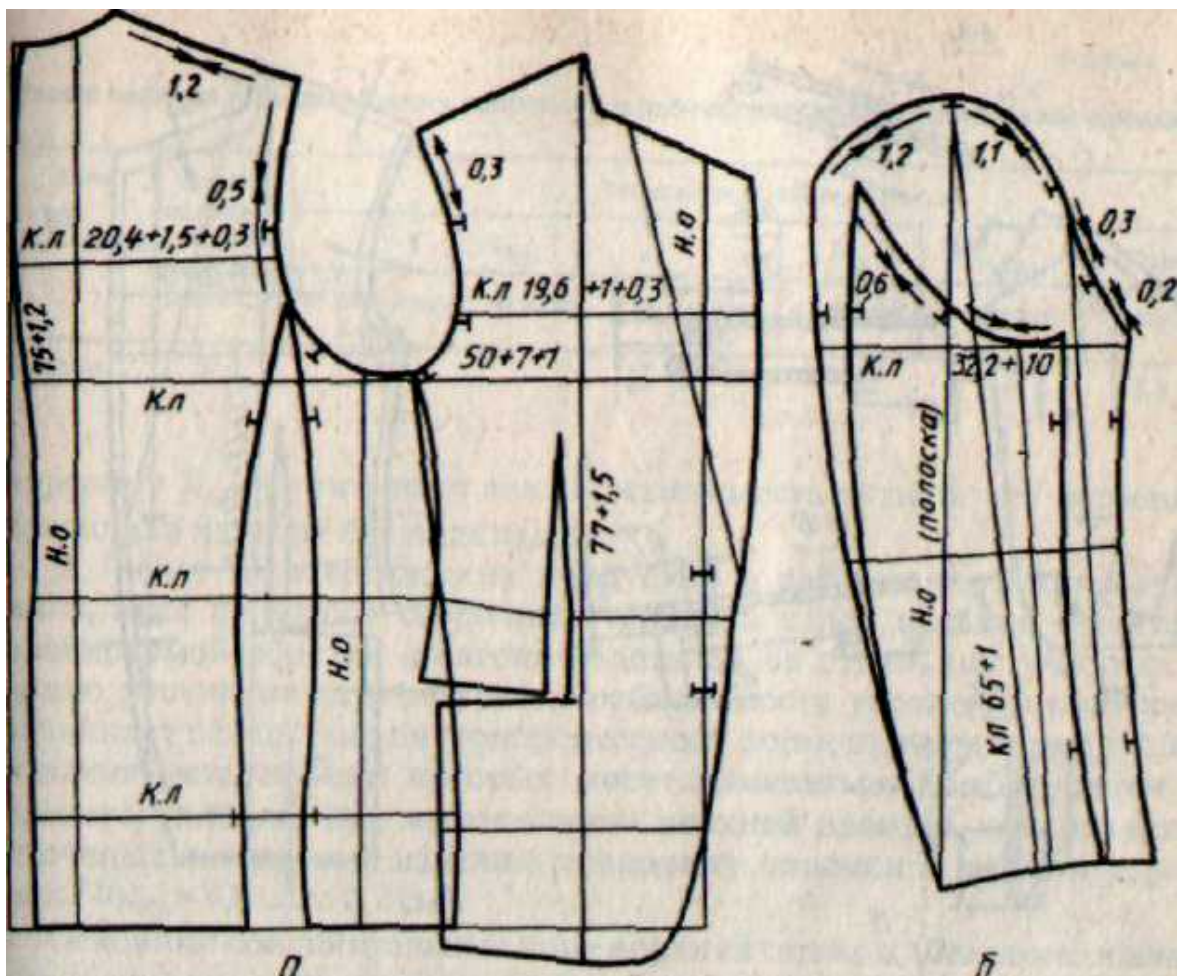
Технический чертеж конструкции пиджака: *а* — спинка и полочка, *б* — рукав
